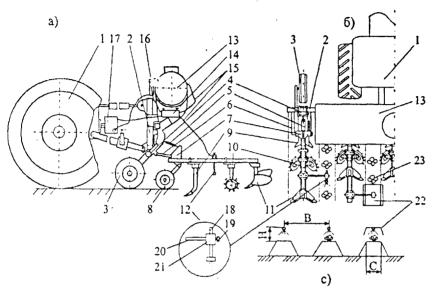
Агрегат для междурядной обработки и ленточного внесения гербицидов; а) вид сбоку; б) вид сверху; с) параметры обрабатываемой поверхности; 1- трактор; 2 - рама культиватора; 3 - колесо ходовое; 4 - кронштейн передний; 5- вит регулировочный; 6 - тяга; 7 - кронштейн задний; 8 - колесо опорное; 9 - стойка с рыхлительной лапой; 10 - борона роторная; 11 - корпус окучивающий; 12 - распыливающий рабочий орган; 13 - емкость для рабочего раствора; 14 - регулятор давления; 15 - всасывающая и нагнетательная коммуникации; 16 - фильтр; 17 - насос шестеренный; 18 - штанга вертикальная; 19 - фиксатор; 20 - штанга горизонтальная; 21 - втулка направляющая; 22 - устройство ветрозащитное; 23 - возделываемые растения
